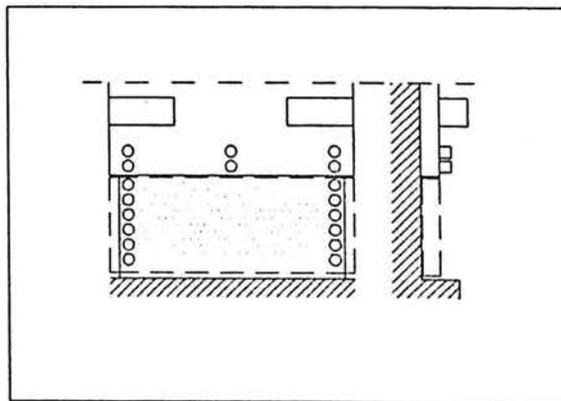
Vorhandener Bauraum für die zu konstruierende Grundplatte
